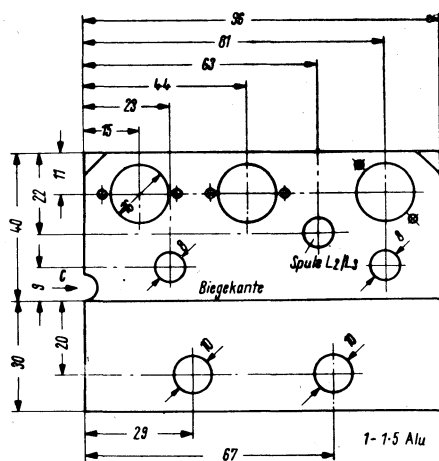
d (links). Maßskizze für das Chassis des Fuchsjagdempfängers
